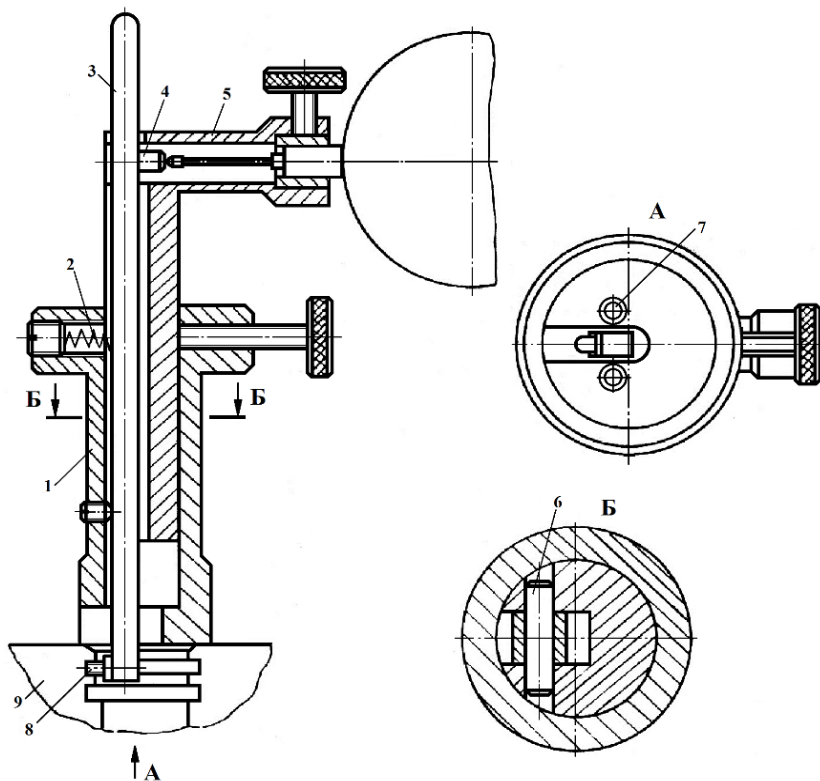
Приспособление для контроля биения канавок относительно базового отверстия
